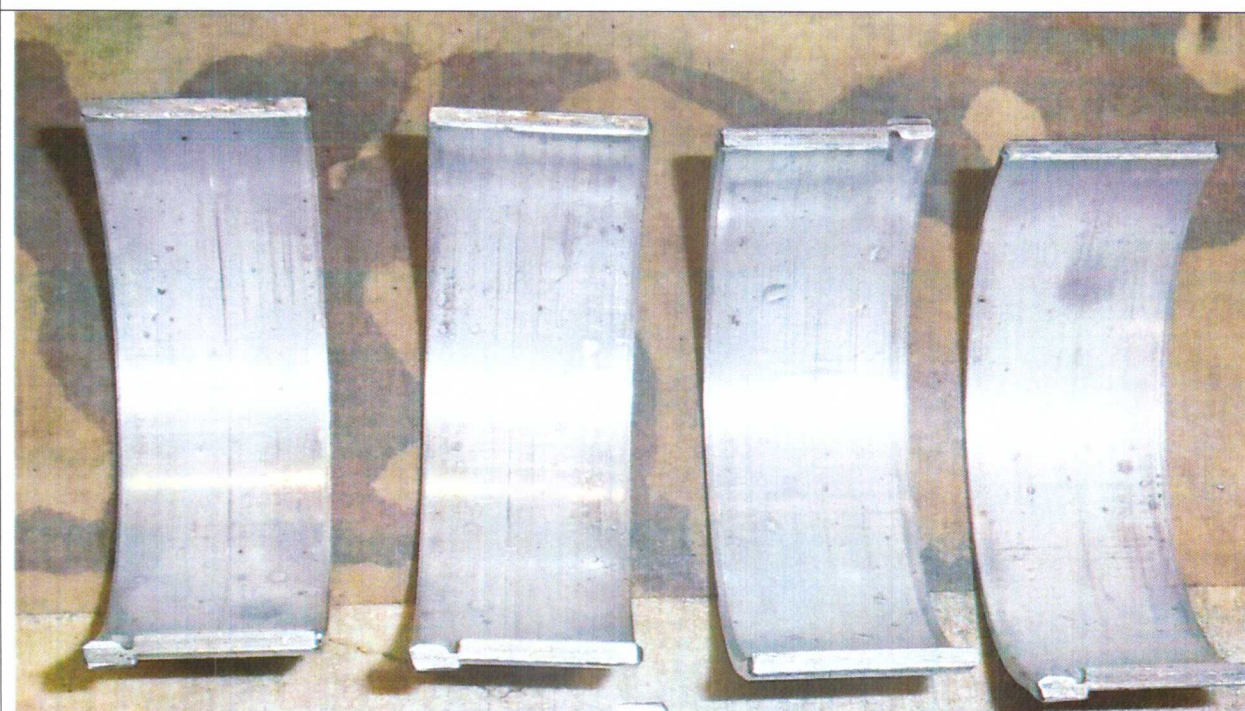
Внешний вид рабочей поверхности верхних вкладышей шатунных подшипников коленчатого вала по окончании длительных испытаний двигателя при работе на базовом масле Castrol EDGE с добавкой нанокompозита Amortect PROOF
